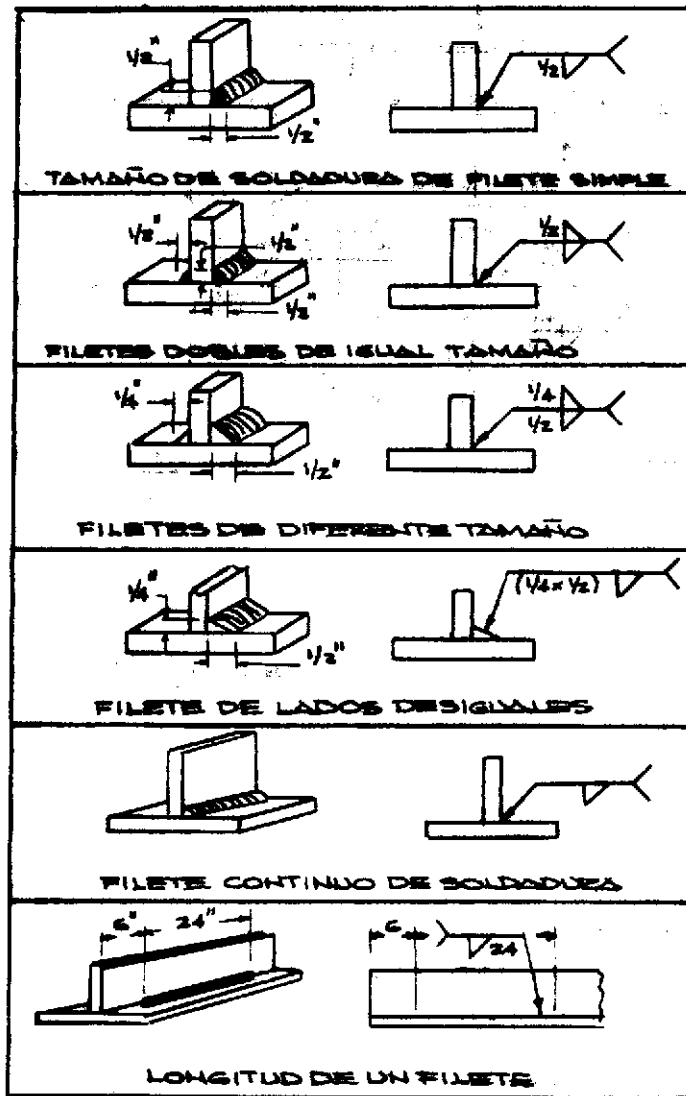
EJEMPLOS DE SOLDADURAS TÍPICAS DE FILETE Y SÍMBOLOS CORRESPONDIENTES.
